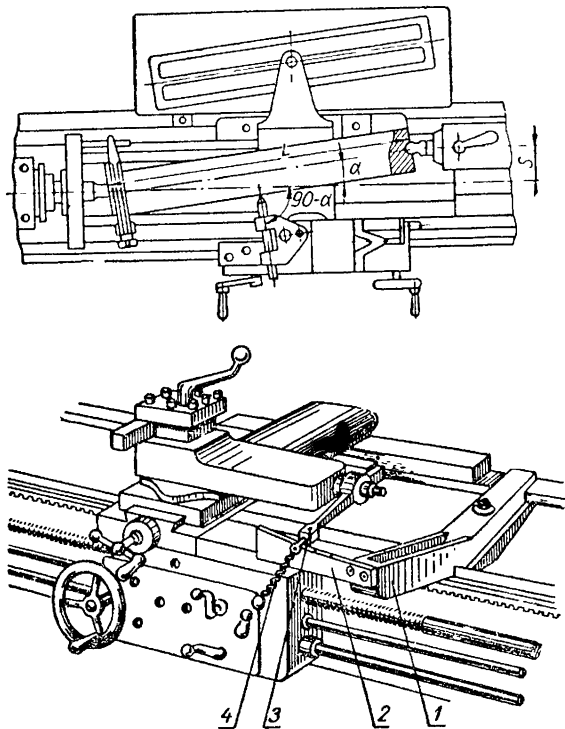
Приспособление для парезания резьбы с переменным шагом.
